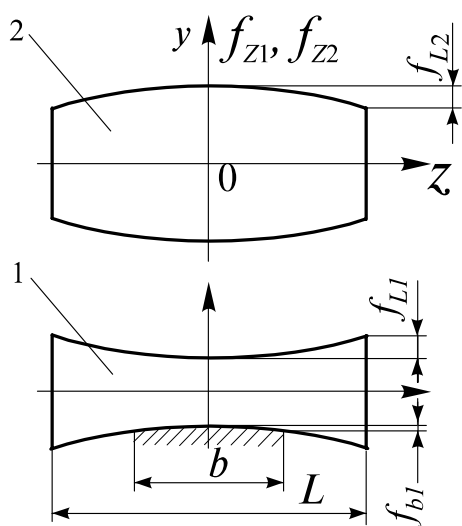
Сопряженные рабочий 1 и опорный 2 валки с рабочими профилями (валки условно раздвинуты)
